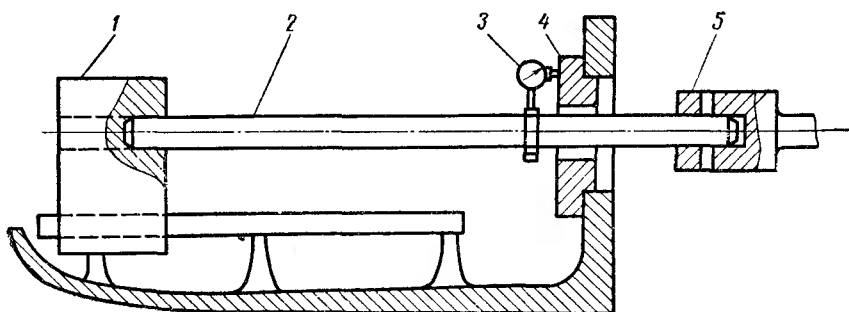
Выверка горизонтально-протяжного станка на совпадение осей
